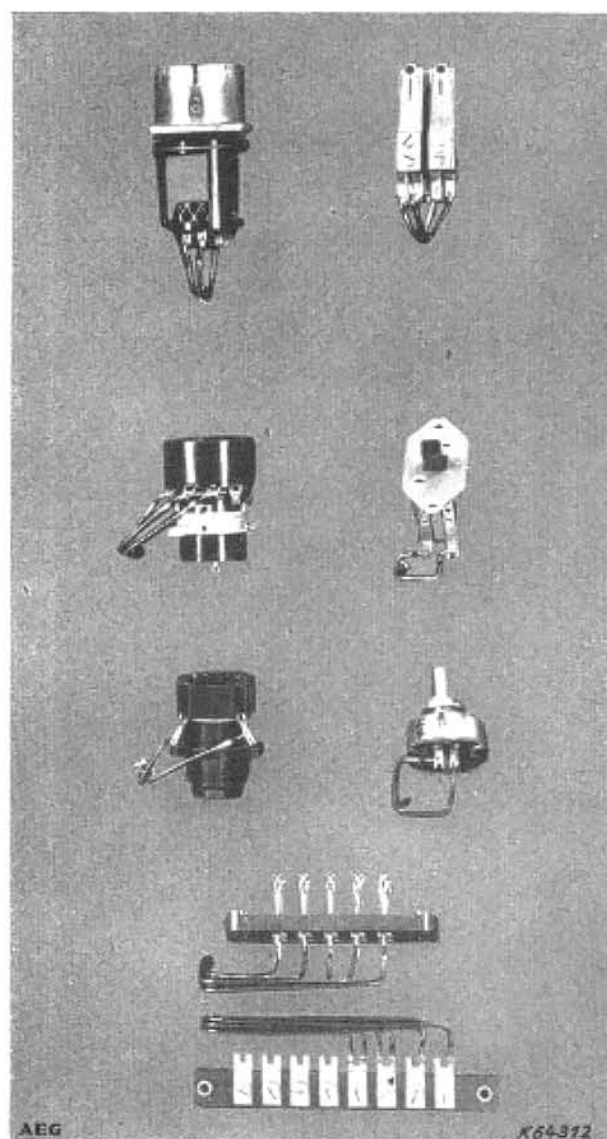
Geschweißte Nachrichtengeräte-Teile.
